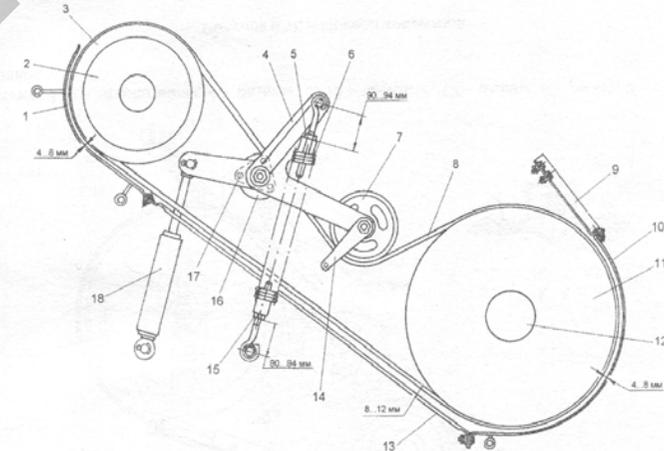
Механизм включения привода транспортера наклонной камеры: 1, 9, 10, 13 — шитки; 2, 3, 11 — шкивы; 4 — рычаг; 5, 15, 17 — гайки; 6 — пружина; 7 — натяжной ролик; 8 — ремень; 12 — вал; 14 — кронштейн; 16 — опора; 18 — гидроцилиндр
